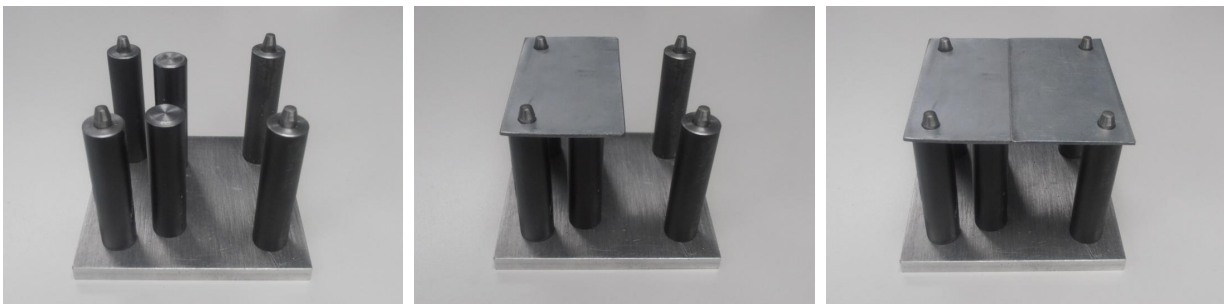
Útil específico desarrollado para soldar chapas en unión a solape.
